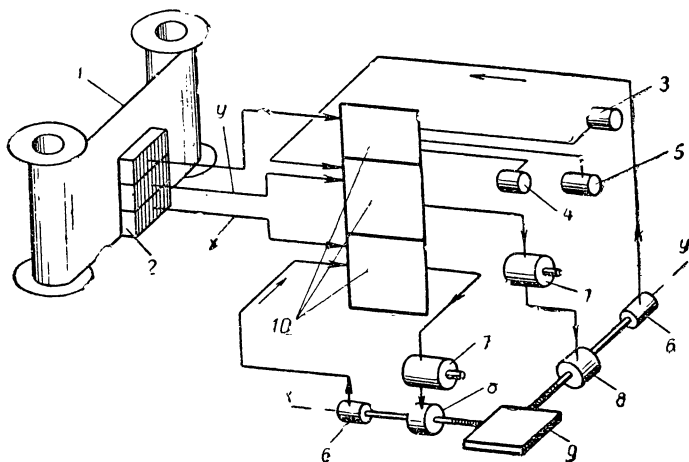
Схема программного управления со следящей системой: 1 — магнитная лента; 2 — головки считывающего устройства; 3 — электродвигатель шпинделя; 4 — электродвигатель насосов смазки; 5 — электродвигатель охлаждения; 6 — сильсин обратной связи; 7 — усилители; 8 — электродвигатели для перемещения столов; 9 — стол фрезерного станка; 10 — электронное устройство.
